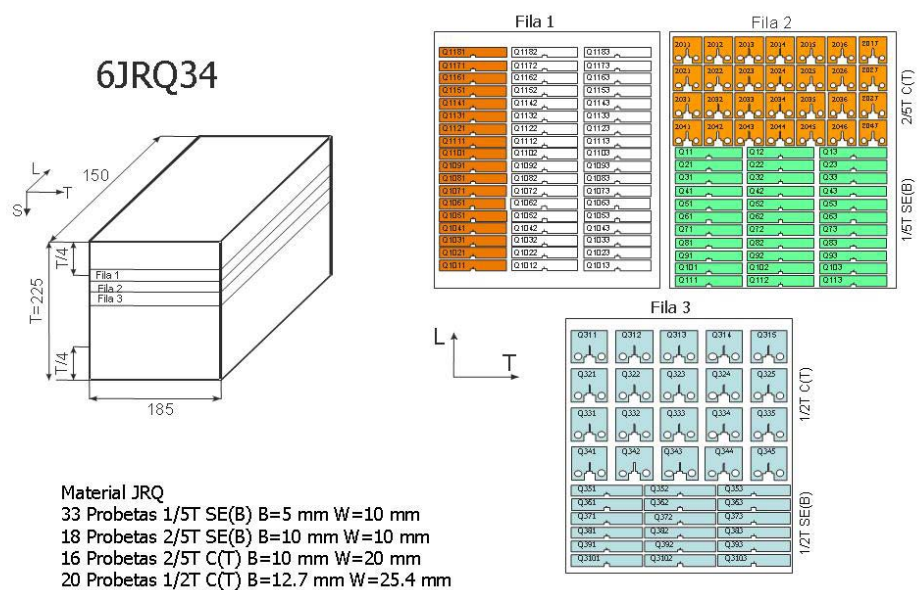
Material JRQ. Bloque 6JRQ34. Mecanizado de probeta
